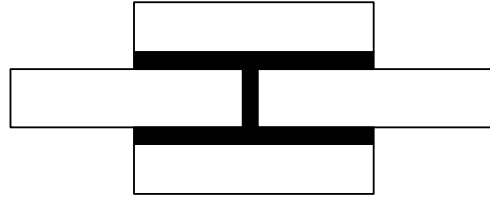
Basamaklı bindirme bağlantı (Stepped lap joint)
